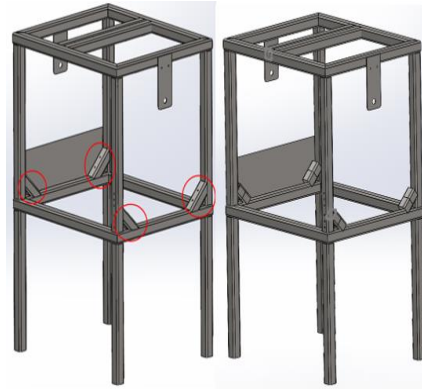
Seccionamiento del elemento estructural de apoyo
